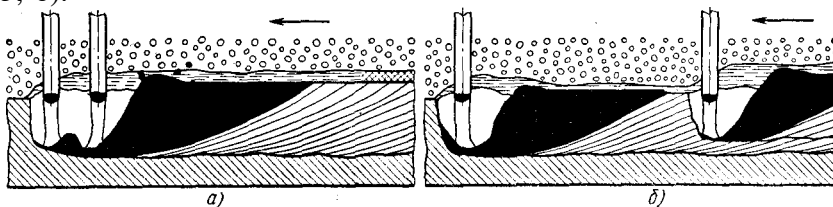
Сварка двумя дугами (стрелкой показано направление сварки):
